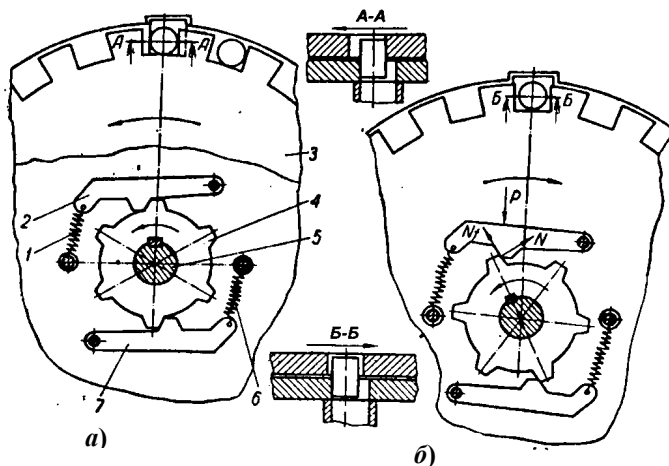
Предохранительный механизм дисковых БЗУ
